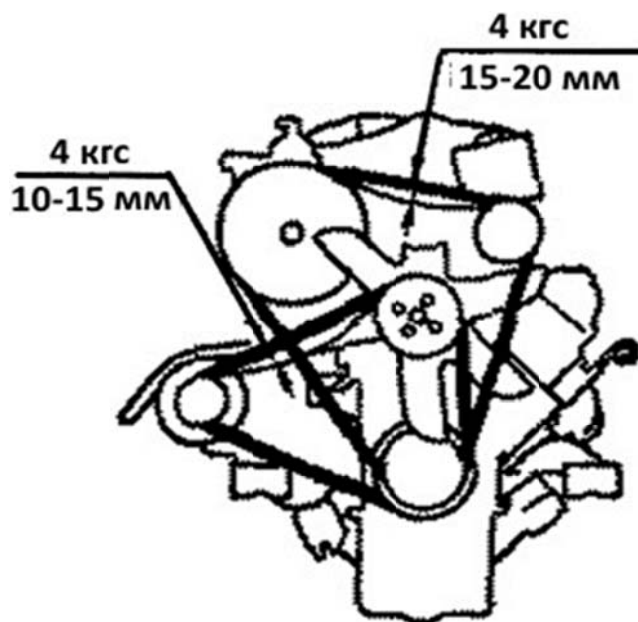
Сема проверки натяжения ремней привода компрессора (насоса гидроусилителя руля) и ремня привода генератора и вентилятора
